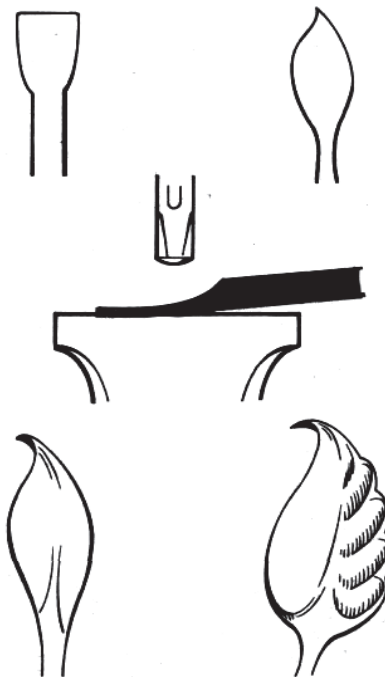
Виготовлення листка з прутка без використання нижника
